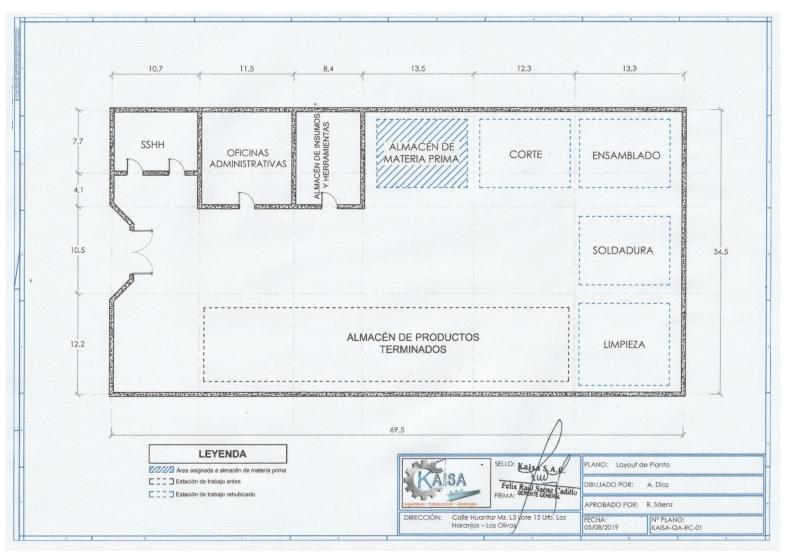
Layout de planta Propuesto para la mejora Fuente: Elaboración propia.
